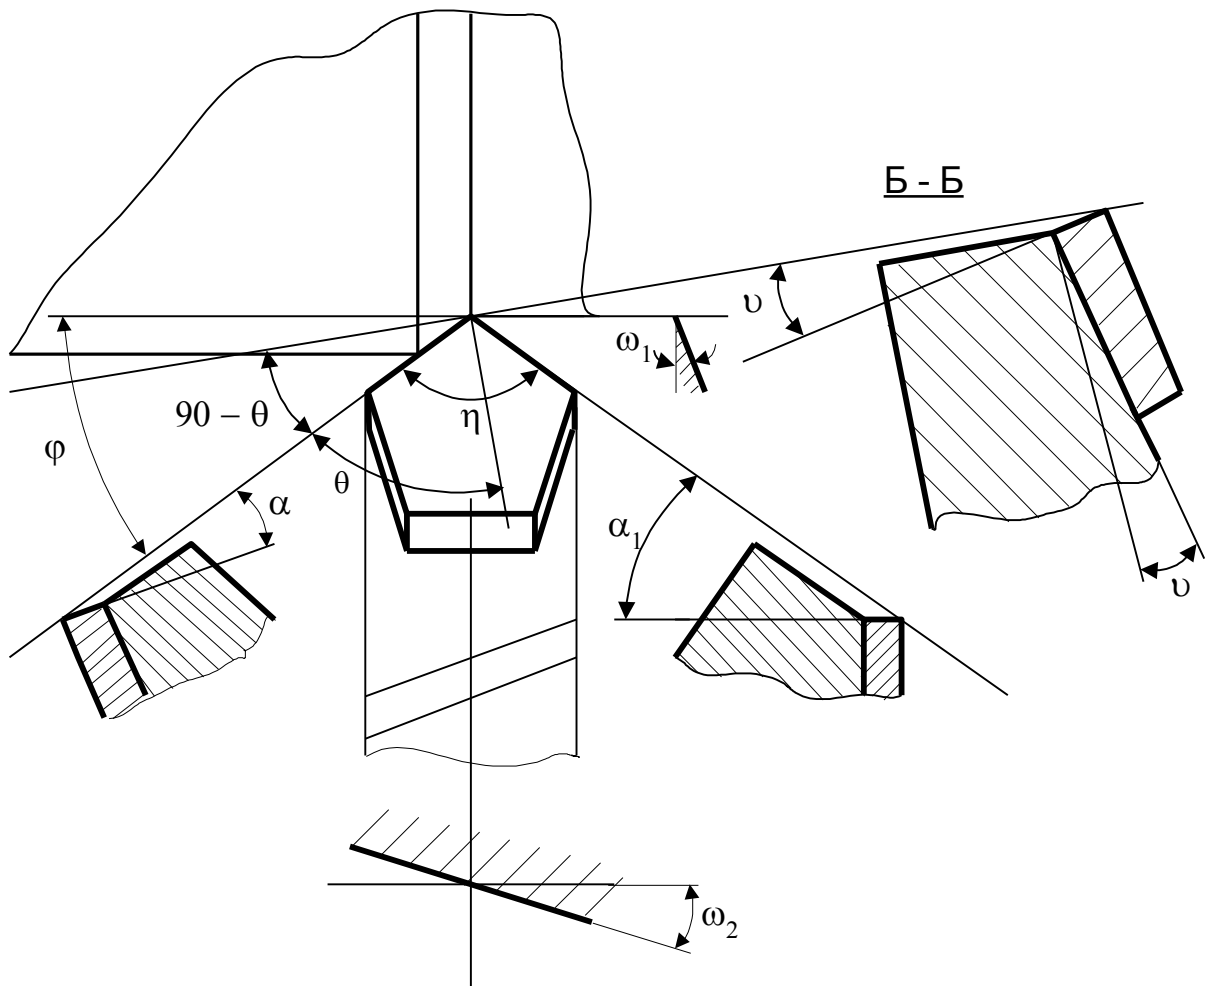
Схема расположения опорной поверхности пластины на державке резца
